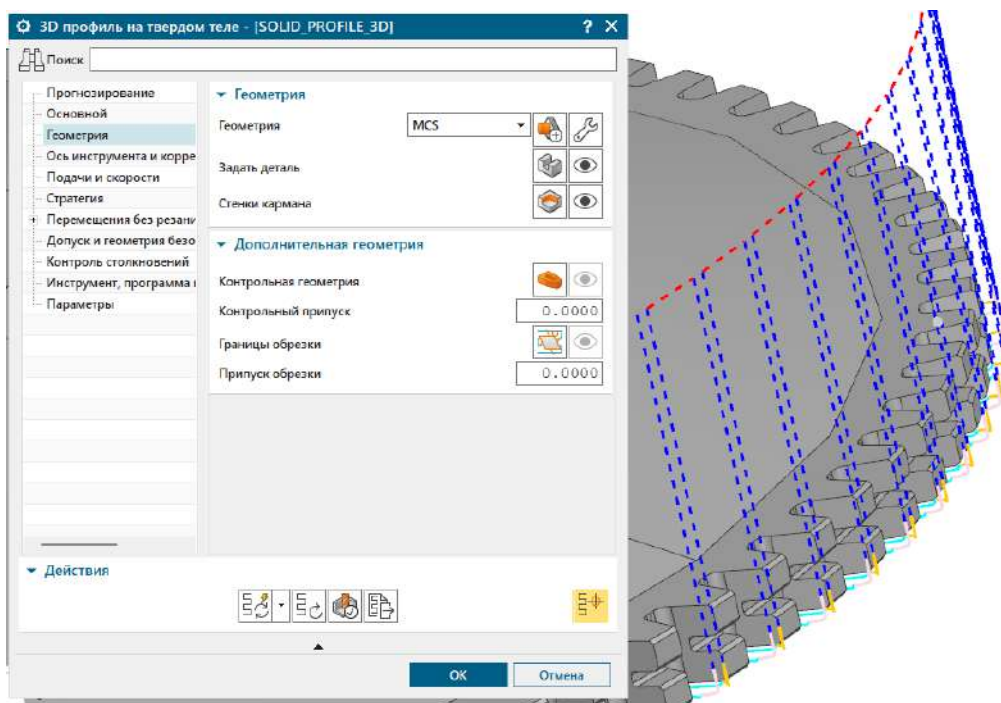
Траектория обработки поверхности на фрезерной операции
